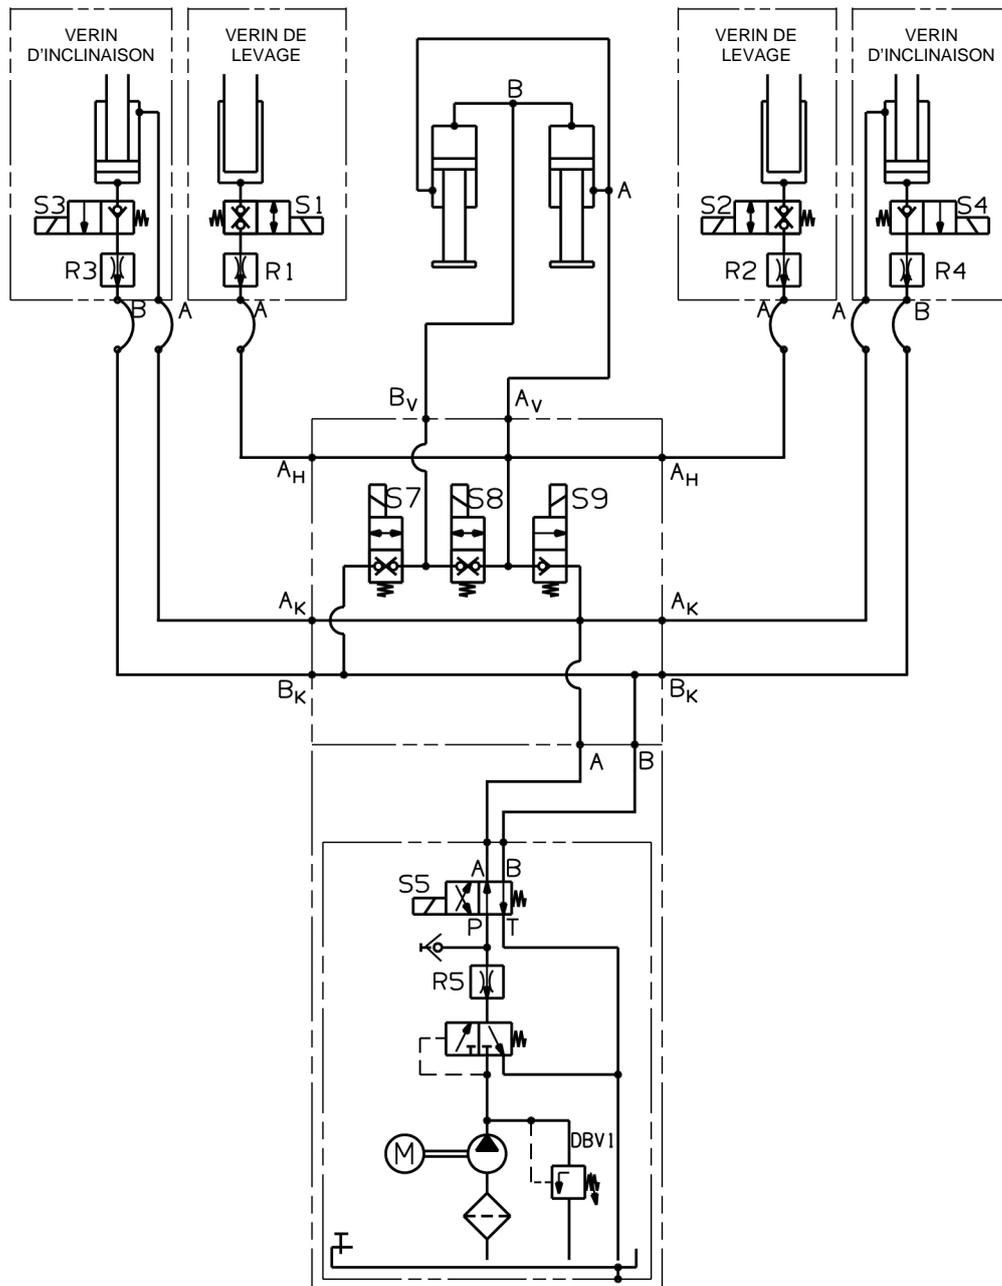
Schéma hydraulique, N° de plan : 96-524.98-01.00-00
